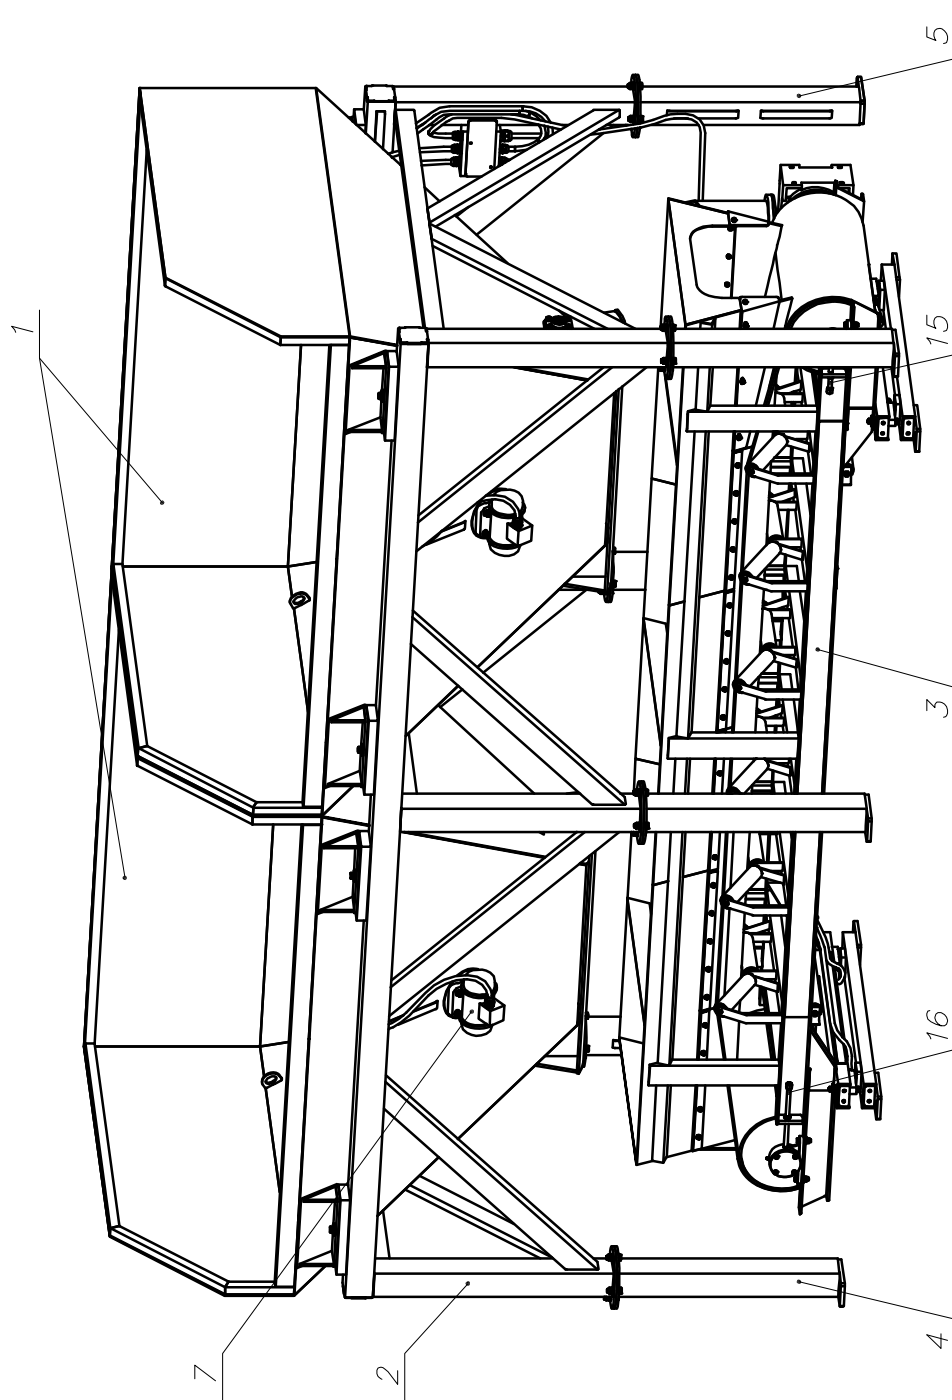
Общий вид дозатора ДЗ-10 вид спереди.
